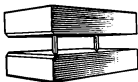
Приспособление для изготовления ножевидного конца стрелки
